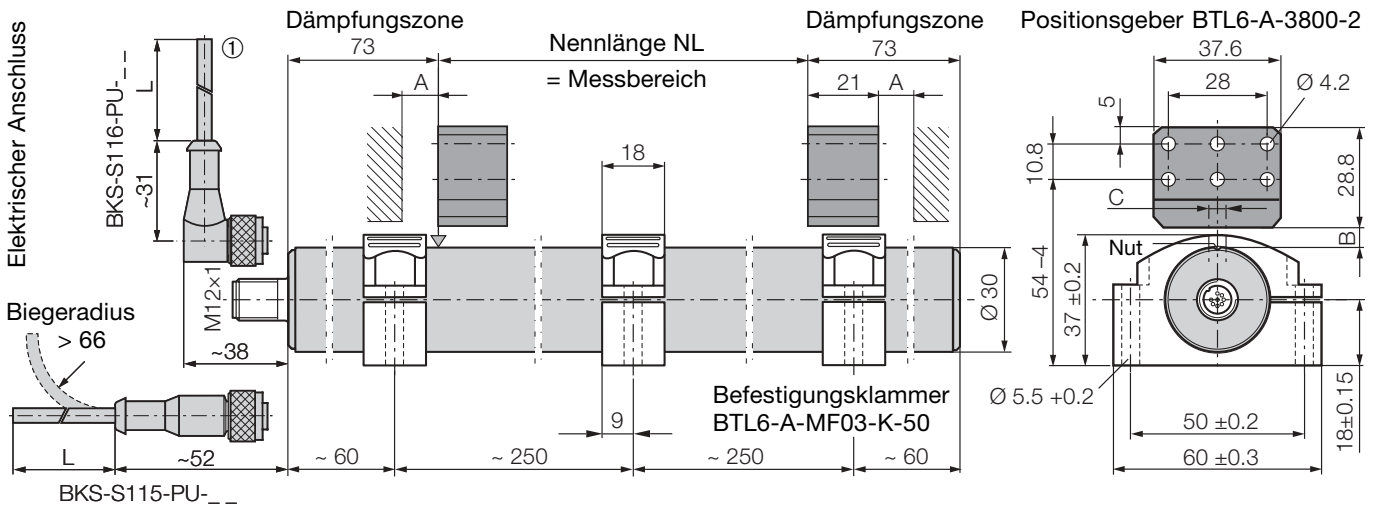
Maßzeichnung (Wegaufnehmer BTL6...A1-S115 mit Positionsgeber BTL5-A-3800-2 und Befestigungsklammern BTL6-A-MF03-K-50)
